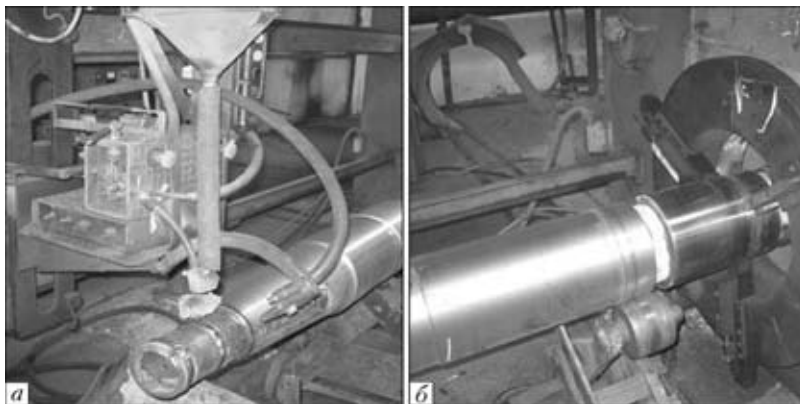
Наплавочная головка установки (а) и установленный в патроне установки
